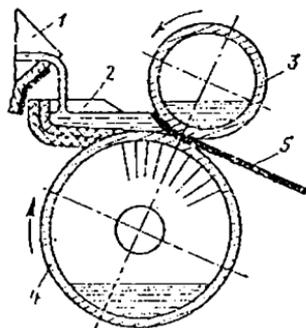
Схема процесса жидкой прокатки: 1 — ковш; 2 — приемник; 3, 4 — валки; 5 — металл
